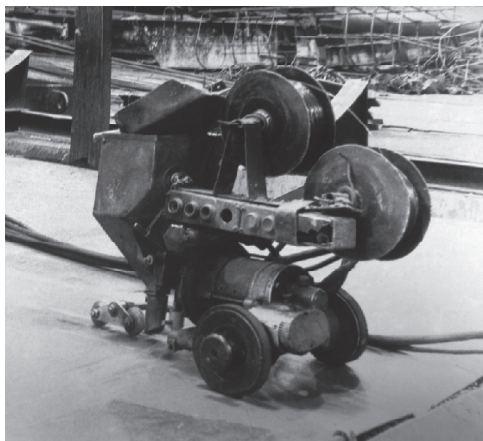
Сварочный аппарат (автомат)
